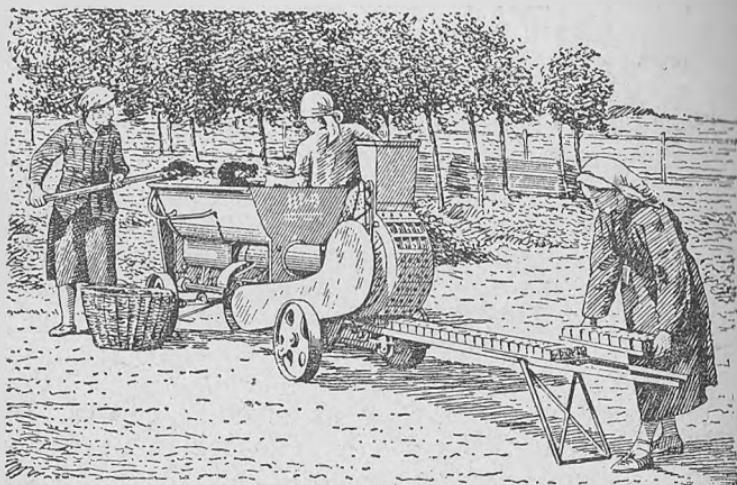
Станок для изготовления торфоперегнойных горшочков.
